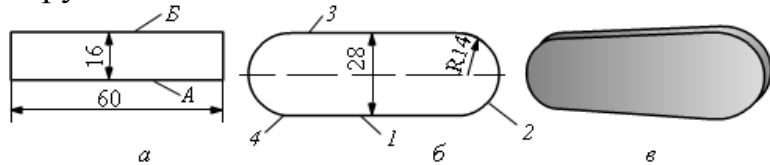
Виготовлення сегментної шпонки: *а* — заготовка; *б* — розмітка; *в* — готова шпонка
